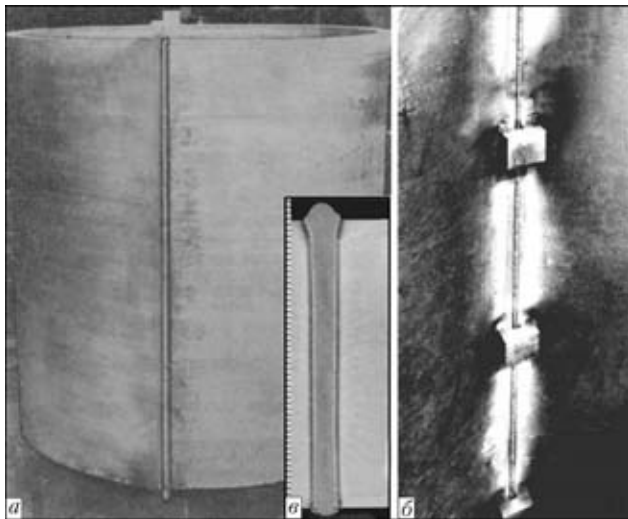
Внешний вид сварной обечайки из сплава М40 (*а*), обратного валика продольного шва (*б*) и микрошлиф соединения (*в*)
